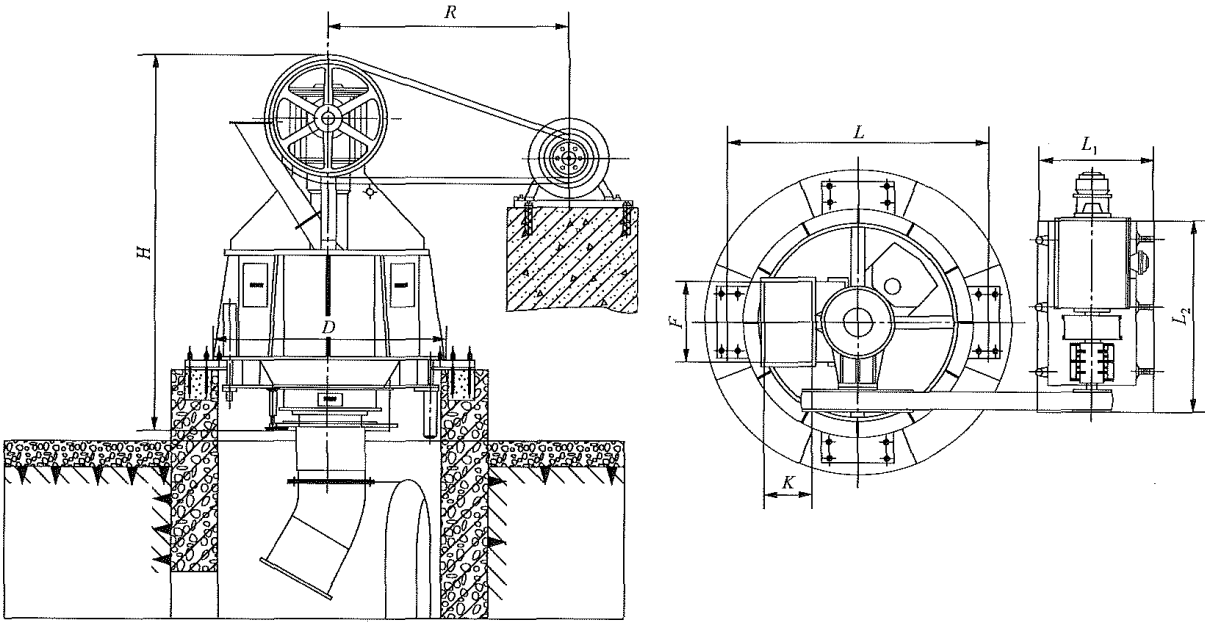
ZMJ 系列柱磨机安装外形尺寸
